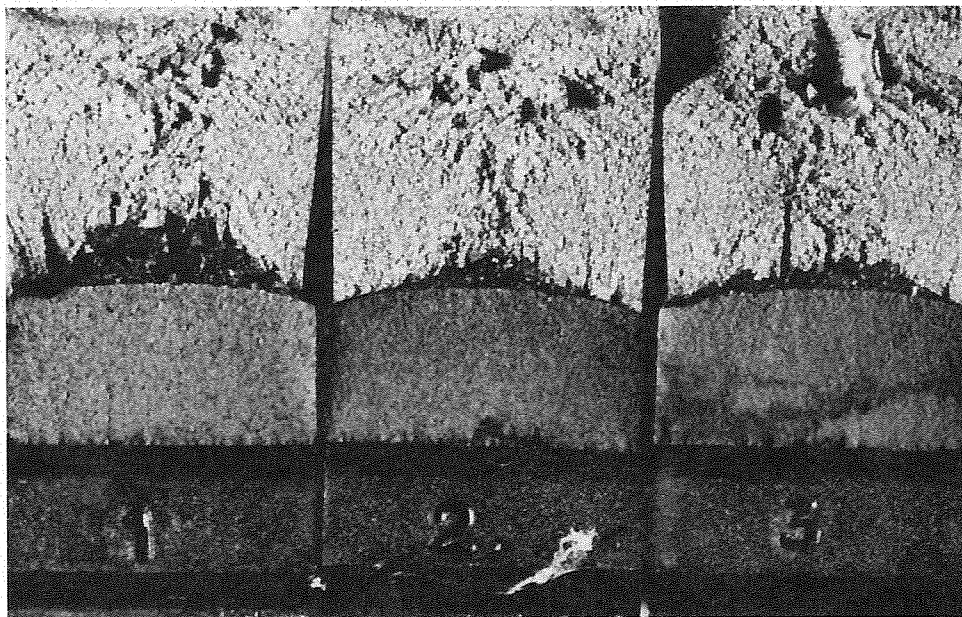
Grietas de fatiga en material base. (probetas 1, 2, 3)
